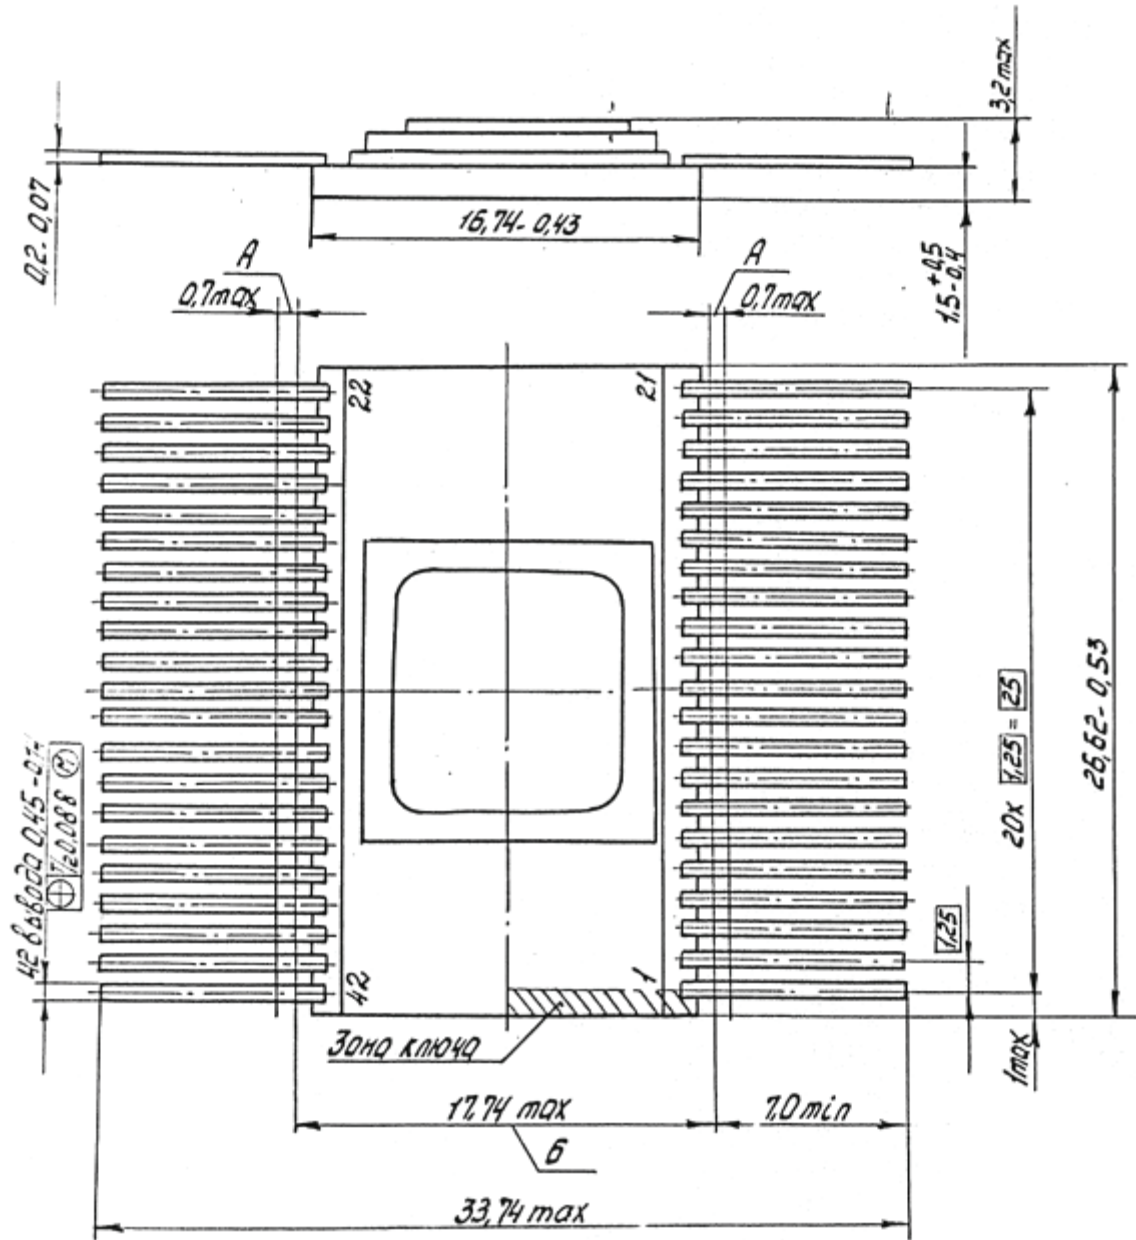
Габаритный чертеж корпуса 429.42-5
